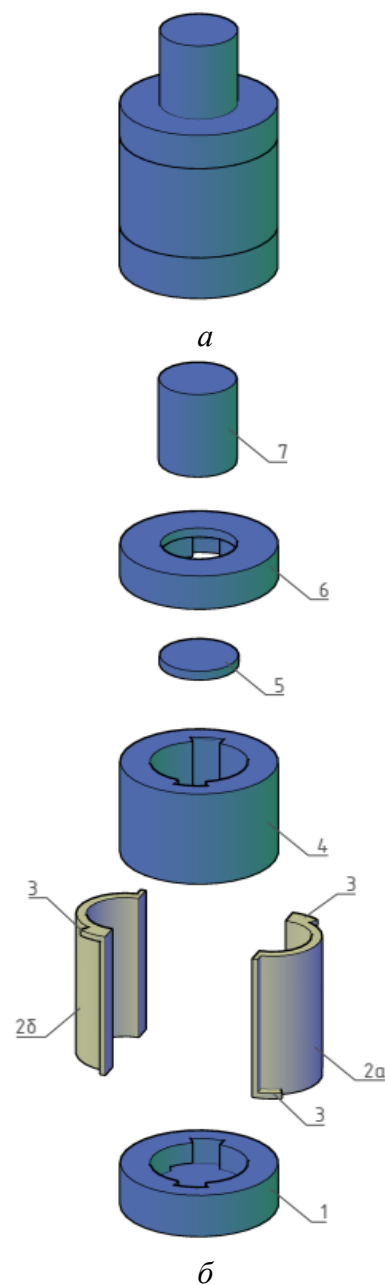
Форма для изготовления образцов: *а* – в собранном состоянии, *б* – детали
